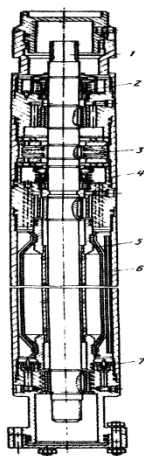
Конструкция протектора гидрозащиты типа Г: 1 – вал; 2, 4 – торцовые уплотнения; 3 – упорный узел (опорная пята); 5 – мешок (диафрагма); 6 – корпус; 7 – обратный клапан.
